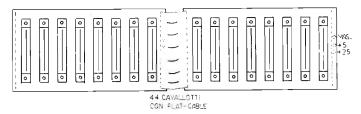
Collegamento di due piastre di fondo per l'espansione.
